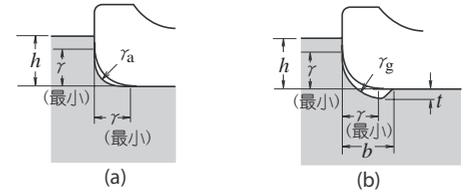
轴承倒角尺寸和轴的圆角尺寸及形状
